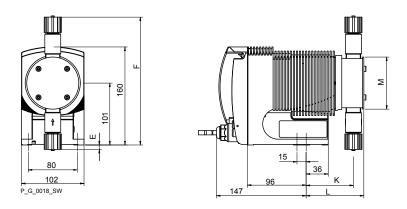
Габаритный чертеж gamma/L, материал ТТТ - размеры в мм
